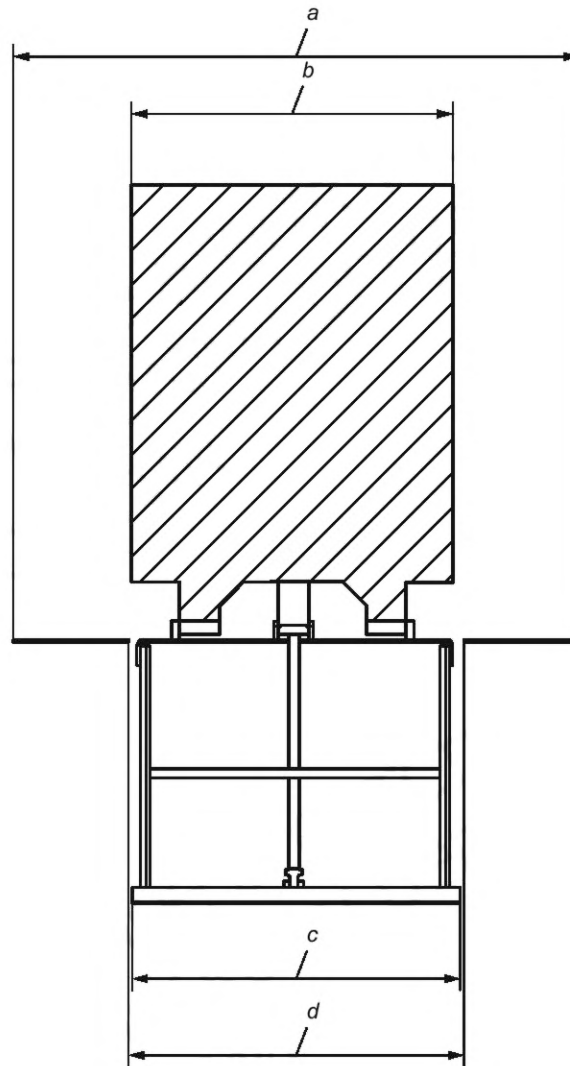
Основные размеры подъемника для ванны в верхнем положении
